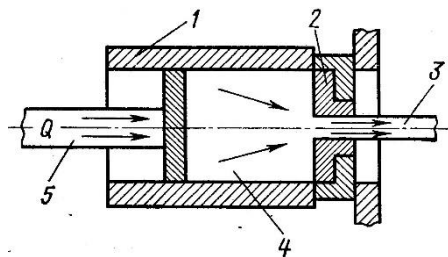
Схема процесса прессования: 1-контейнер; 2-матрица; 3-изделие; 4-слиток; 5-пуансон
